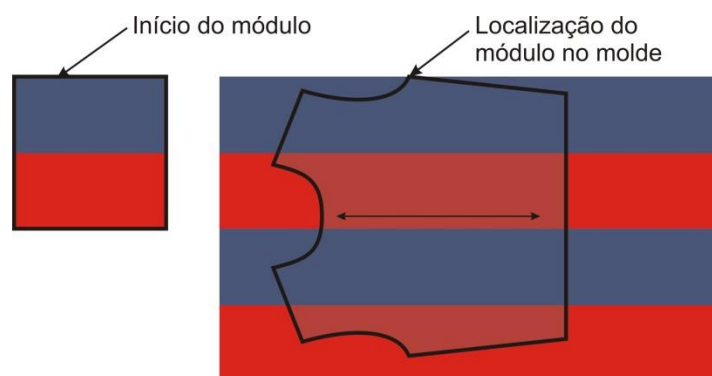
Início do molde coincide com o início do módulo, assim como o final do molde que está na mesma posição do final do módulo
